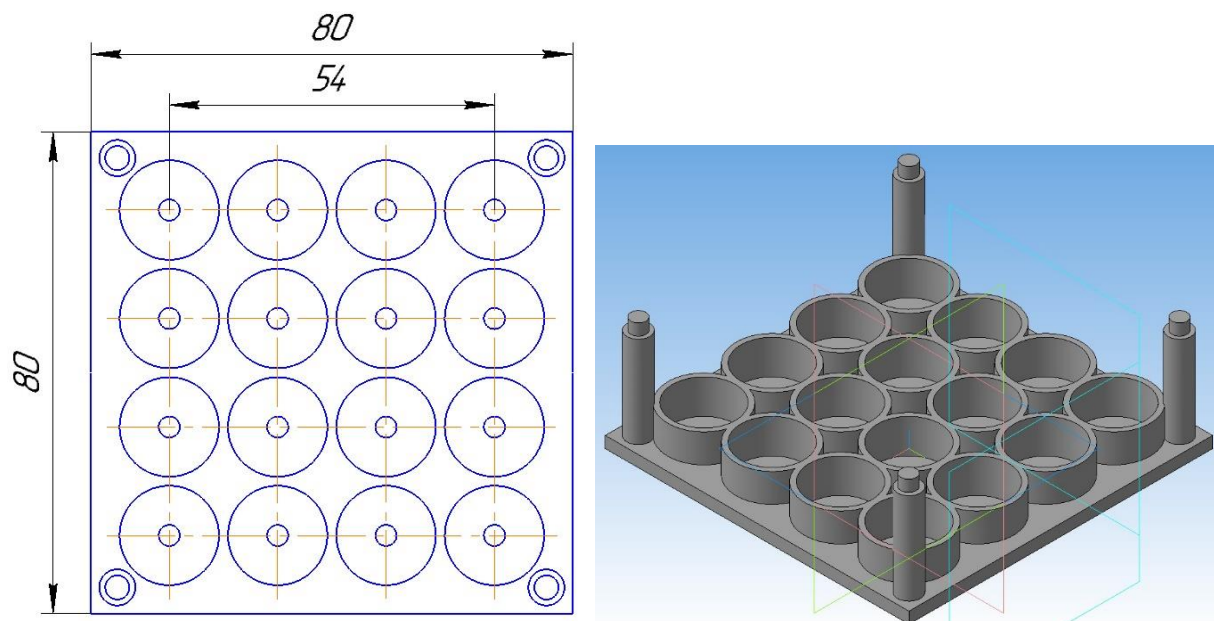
Корпус для крепления катушек. Вид сверху. Вид 3-D модели
